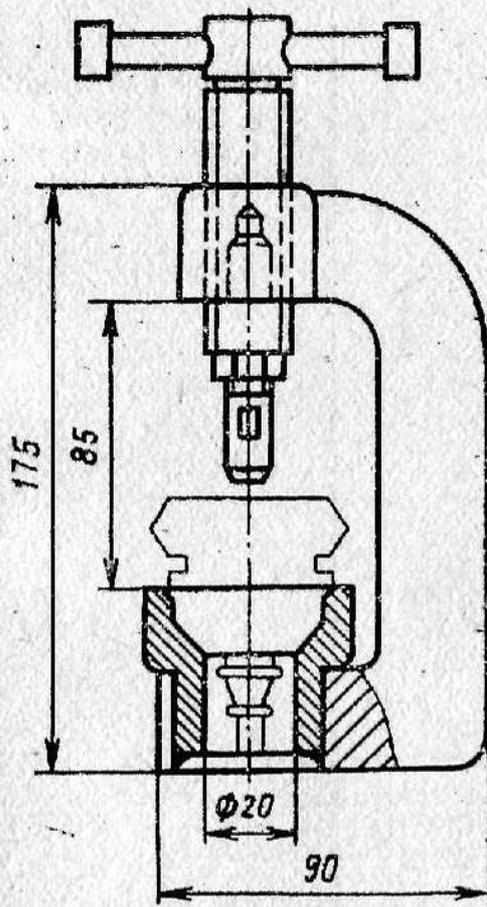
Приспособление для сборки и разборки шаровых шарниров
